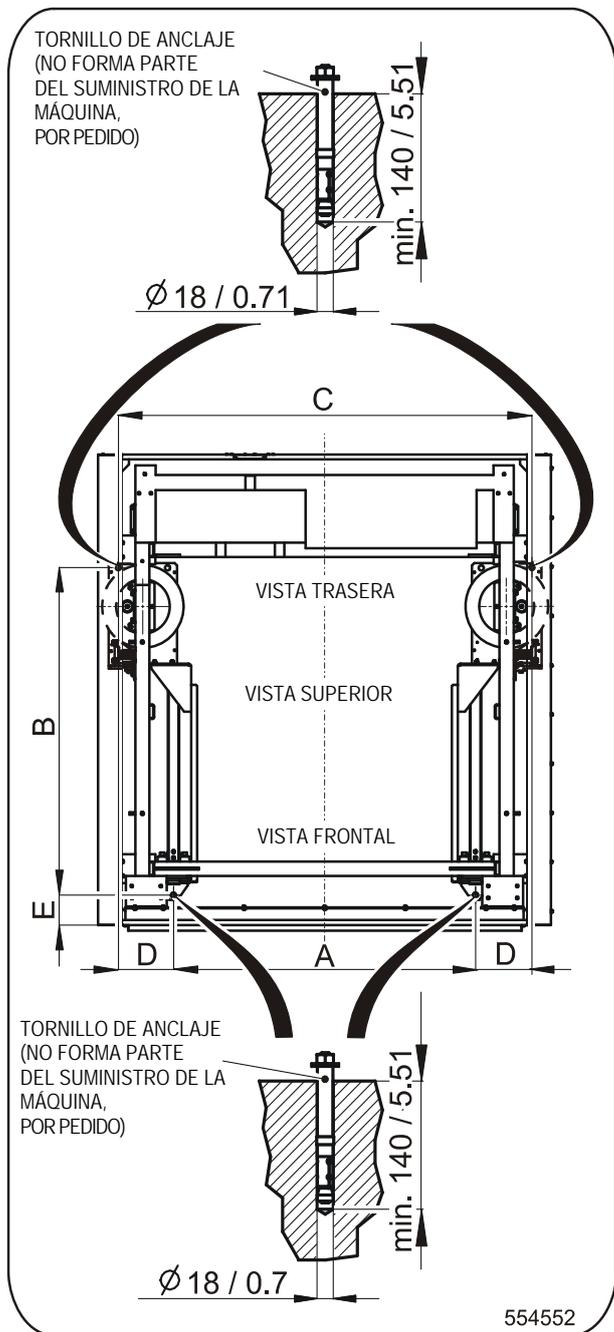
J Máquina 80-100-120 kg / 180-230-275 lbs con la inclinación delantera y sin el sistema de pesado, puesto del taladrado para tornillos de anclaje, (dimensiones en mm / pulgada)
